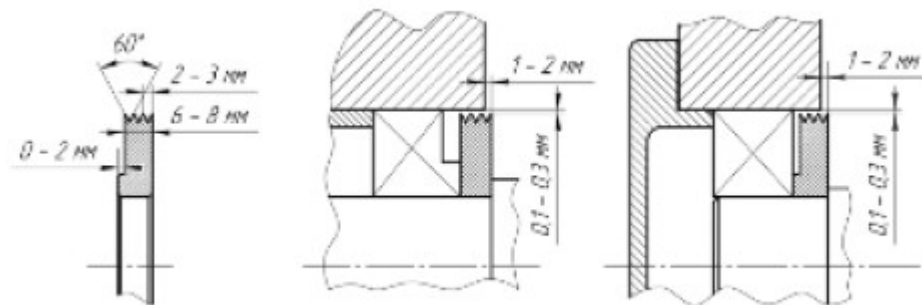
Конструкция мазеудерживающего кольца, подшипниковые узлы с использованием пластичного смазочного материала
